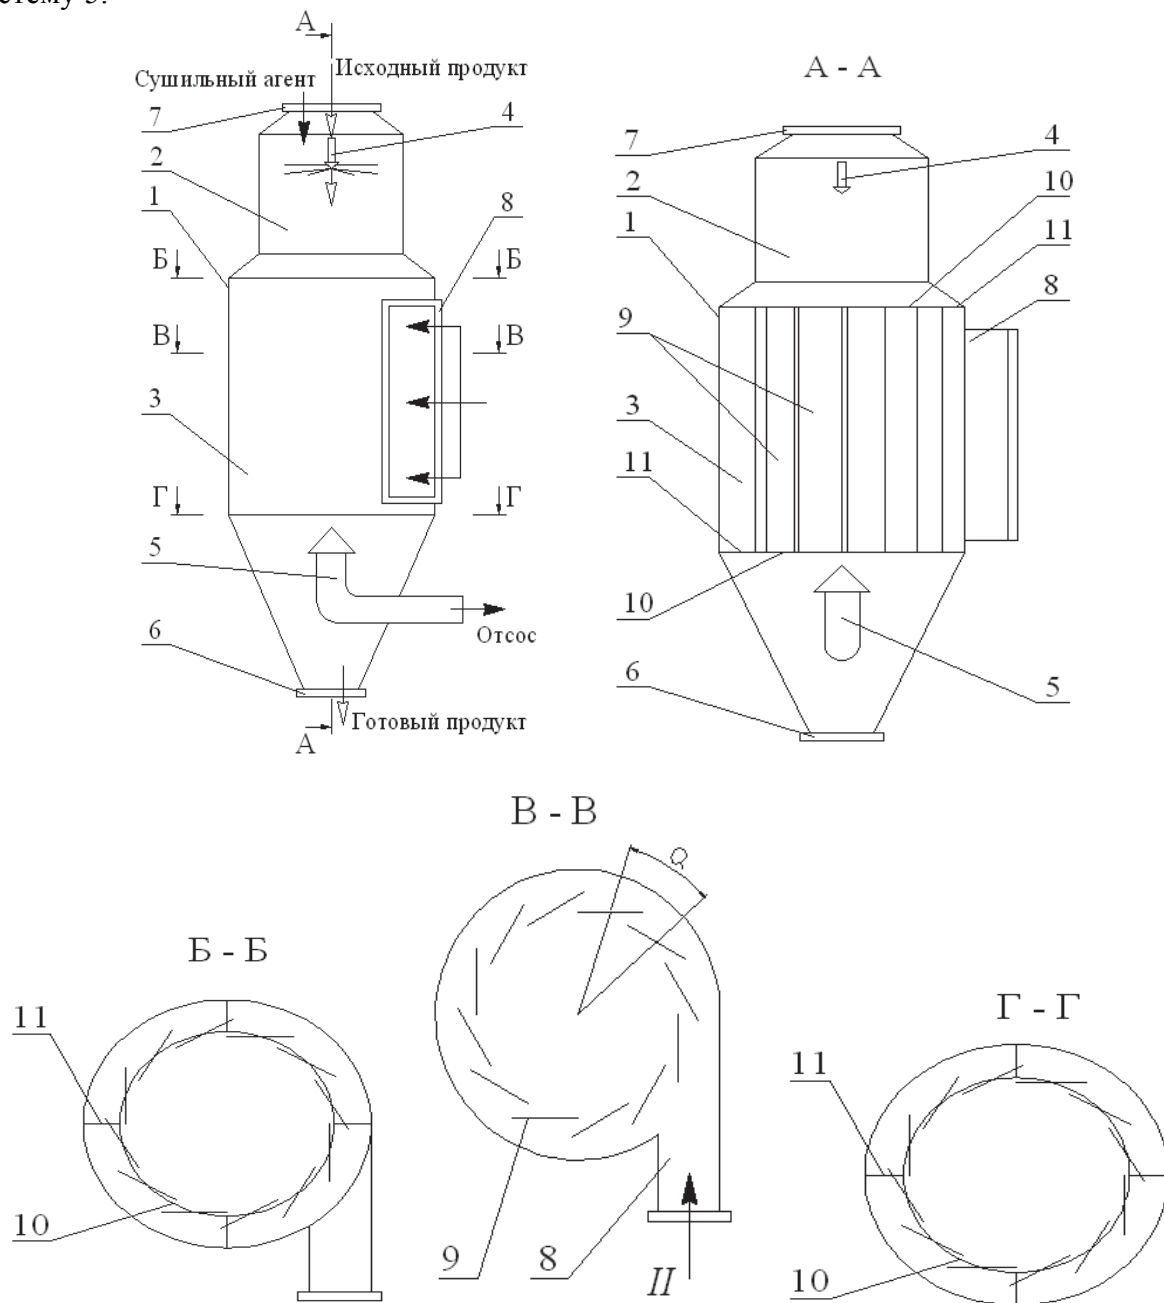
Распылительная сушилка: 1 – сушильная камера; 2, 3 – полые цилиндры; 4 – распылитель; 5 – система отсоса; 6 – узел выгрузки; 7, 8 – патрубок для ввода сушильного агента; 9 – вертикальные прямоугольные перегородки; 10 – крепления; 11 – стержневые крепежные элементы
